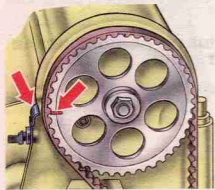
Проверка совпадения установочных меток на шкиве коленчатого вала и крышке масляного насоса
